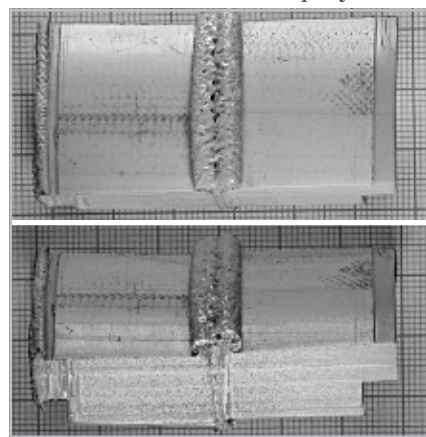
Сварной шов трубного образца из РЕИ, полученный при сварке нагретым инструментом встык
